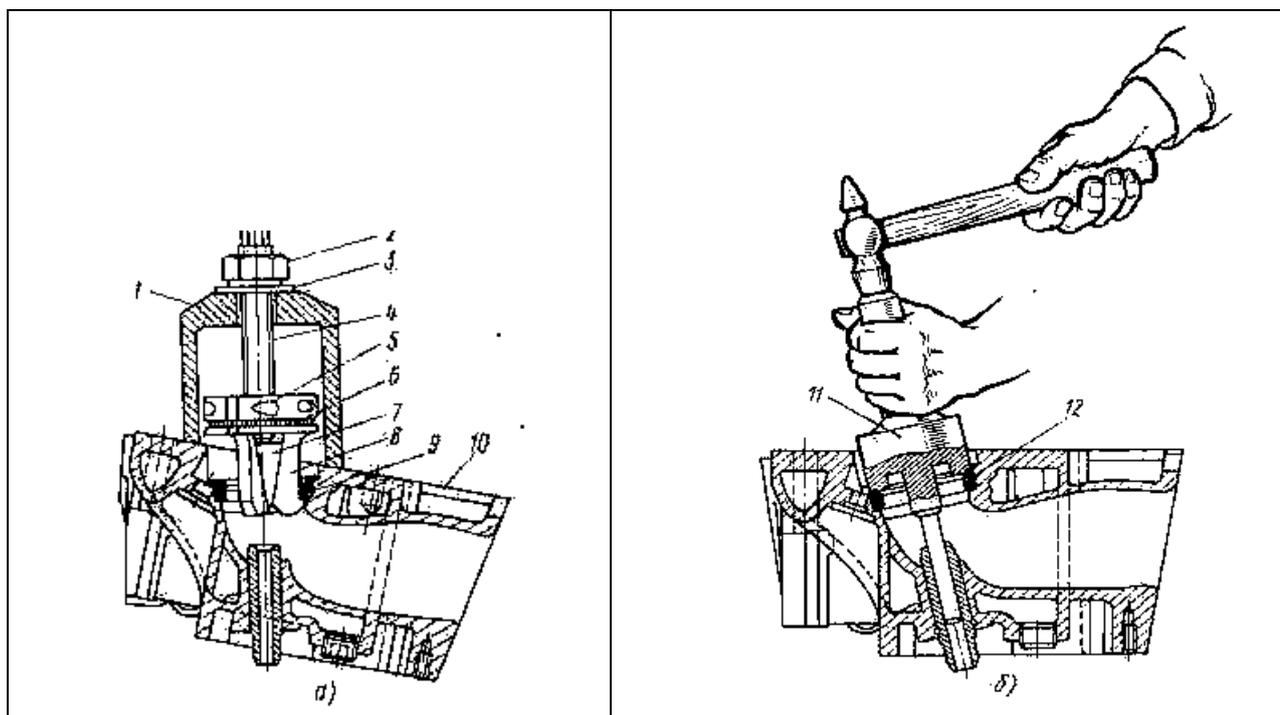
Замена седла клапана: а- впрессовка седла при помощи съемника; б-запрессовка седла; 1-корпус съемника; 2-гайка; 3-шайба; 4-винт; 5-трехгранная гайка; 6-натяжная пружина; 7-конус держателя; 8-держатель съемника; 9, 12-установленные седла; 10-головка цилиндров; 11-колодка
